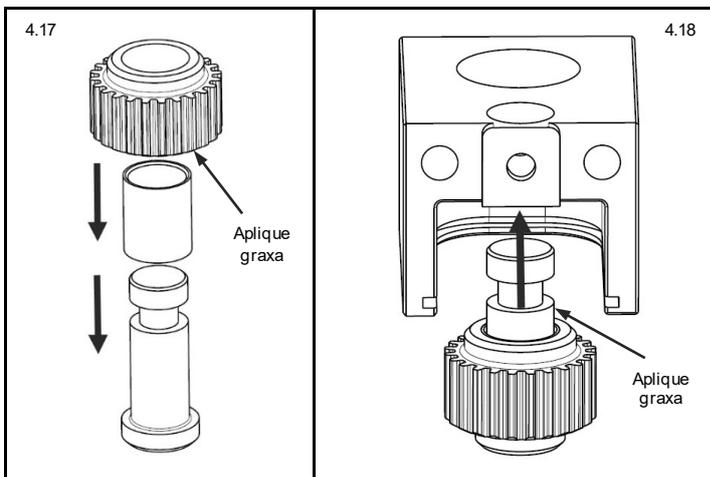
Lubrifique e monte a engrenagem intermediária
